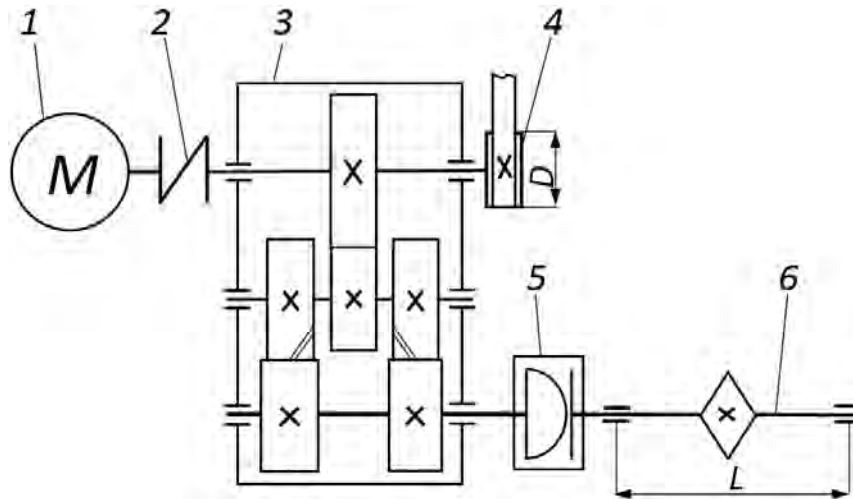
Схема привода скребкового конвейера (вид сверху): 1 – асинхронный электродвигатель; 2 – муфта упругая втулочно-пальцевая; 3 – редуктор двухступенчатый (первая ступень – прямозубая цилиндрическая, вторая – косозубая цилиндрическая с разделенным потоком мощности); 4 – шкив вспомогательной ременной передачи для облегчения запуска двигателя в экстремальных условиях; 5 – муфта кулачково-дисковая; 6 – приводной вал с приводной звездочкой
